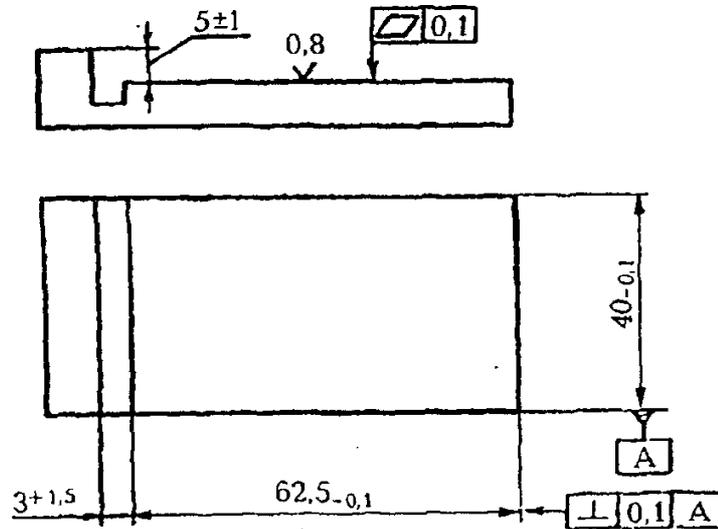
Нажимная пластинка для передачи нагрузки на половинку образца-балочки
